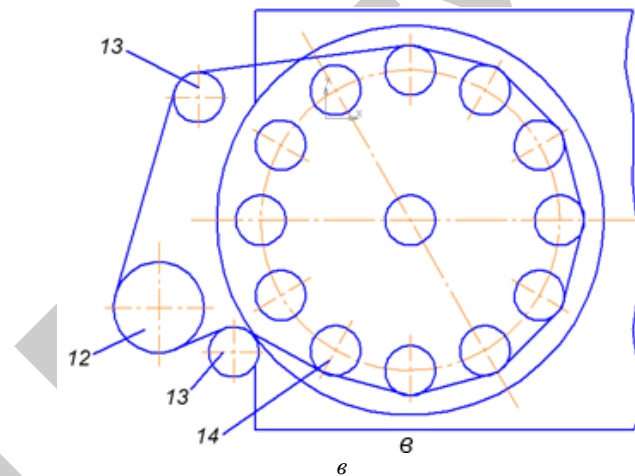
Схема установки для МАО поверхностей деталей фасонной формы:
